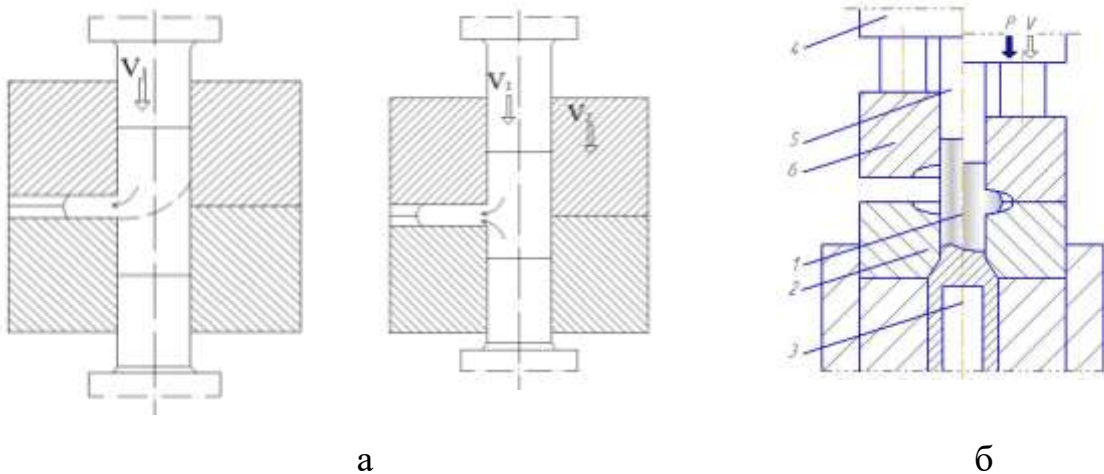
Способи поперечного видавлювання з регульованою подачею металу в порожнину матриці
